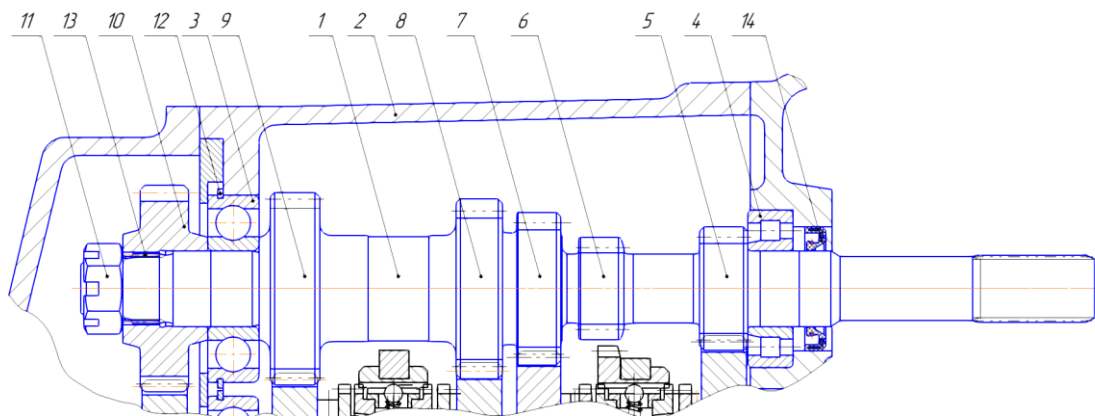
Фрагмент узла первичного вала коробки переключения передач для Lada Priora
